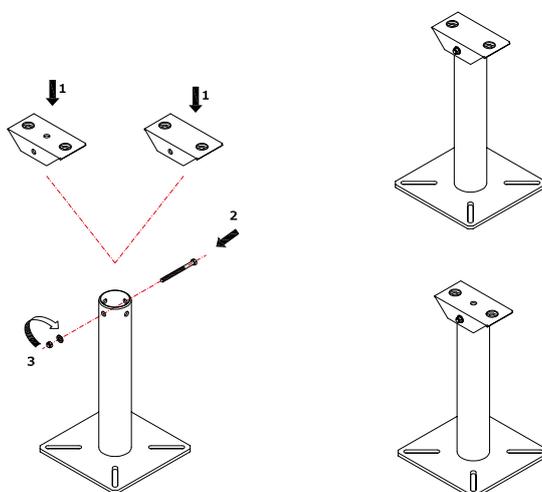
Assemblaggio del Palo Economy* con terminale Cod.000305/000038
